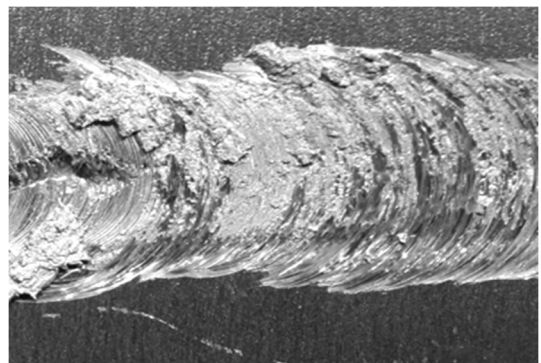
Лицевая поверхность шва, выполненного СТП на сплаве 1565ч с перегревом металла (×1,3)
